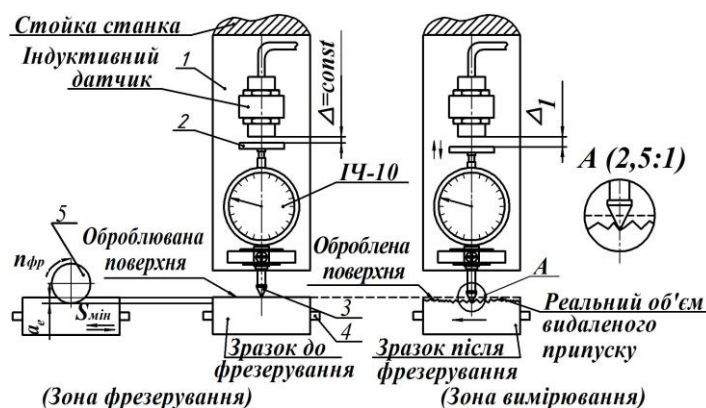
Схема пристрою для вимірювання видаленого припуску і профілю обробленої поверхні: 1 – основа; 2 – п'ята; 3 – вимірюючий наконечник; 4 – ПС ТЕД; 5 – фреза.
